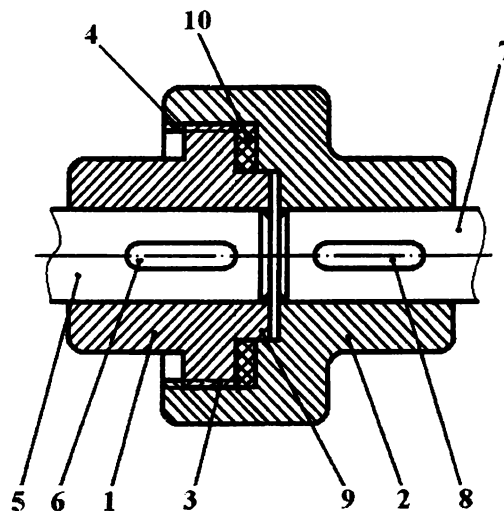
Схема фланцевої різьбової муфти з фрикційною шайбою
